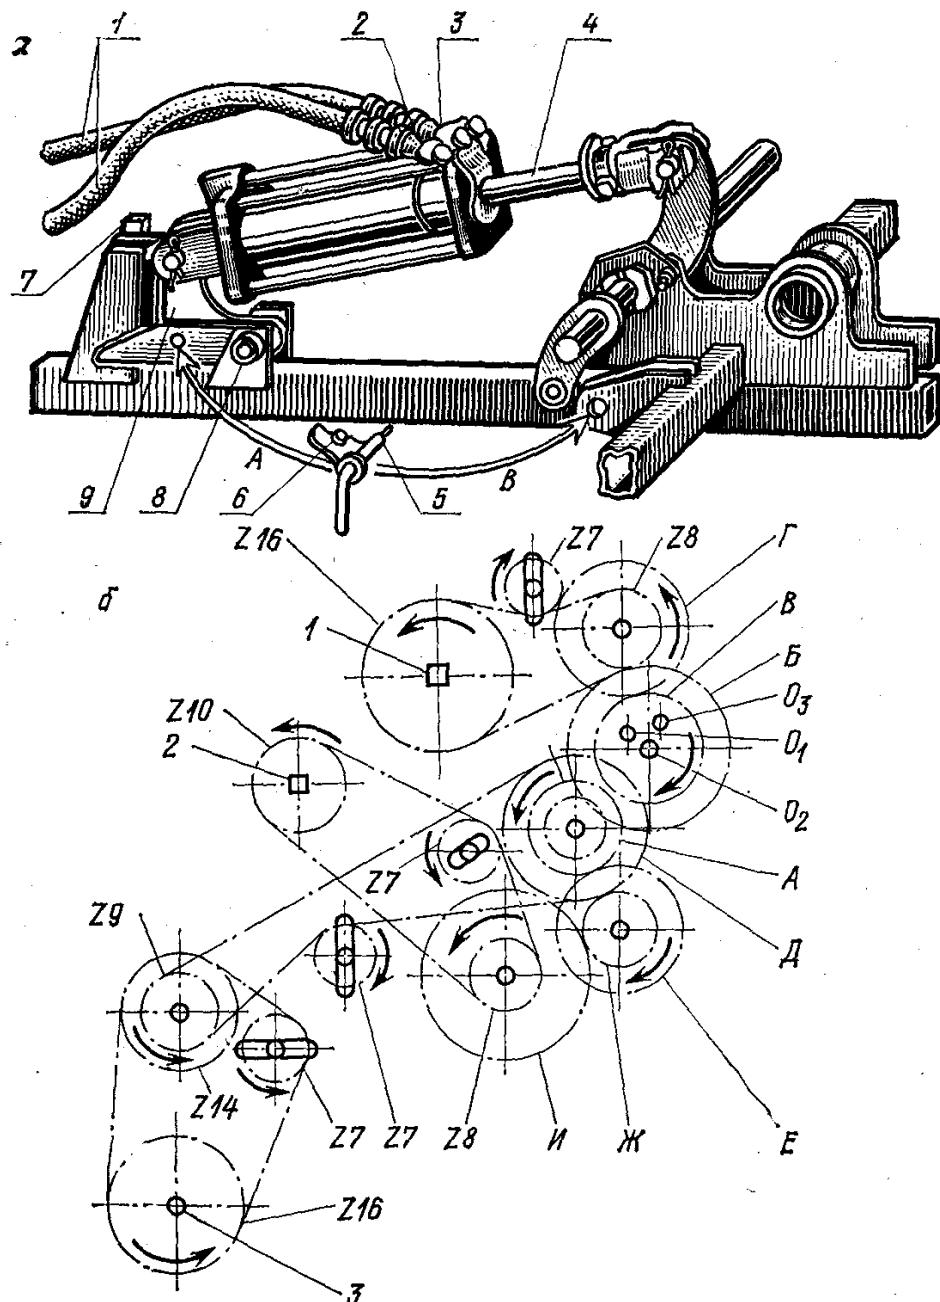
Устройство узлов сеялки СЗ-5,4: а - установка гидроцилиндра и штыря; б - схема механизма передач
